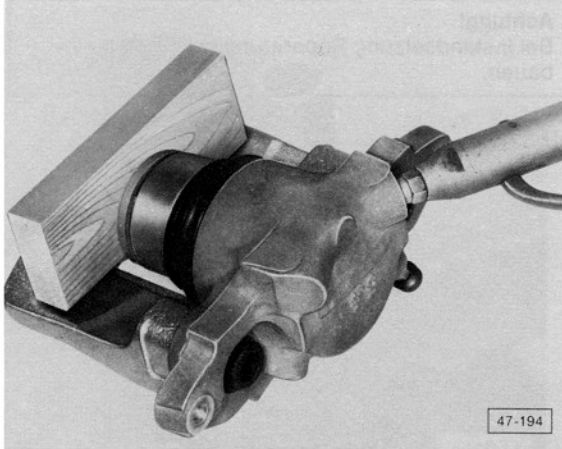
Kolben mit Druckluft aus dem Zylinder drücken
